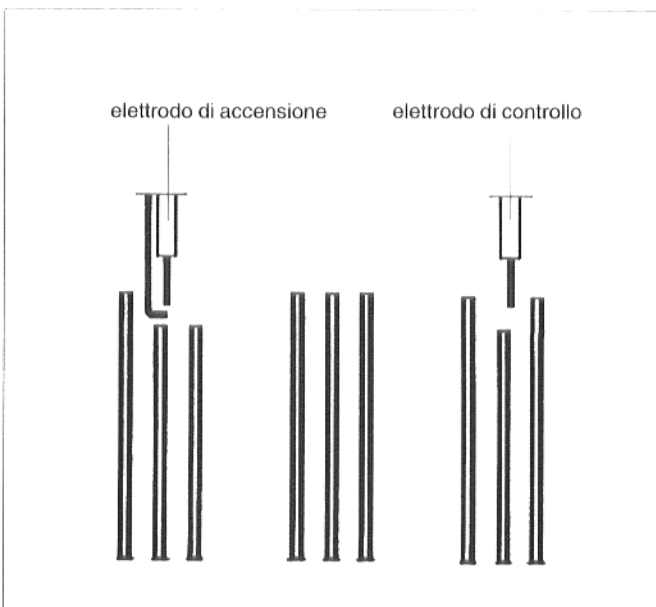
Disposizione delle barrette di raffreddamento*, vista dall'alto
